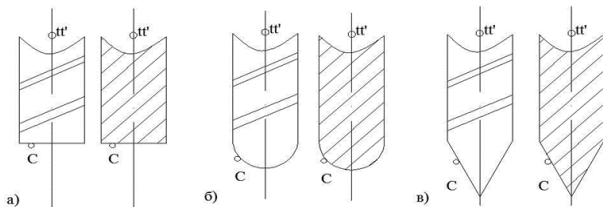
Схема торкання фрези з контрольованою геометрією: а) кінцевої циліндричної; б) сфероциліндричної; в) конічними фрезами
